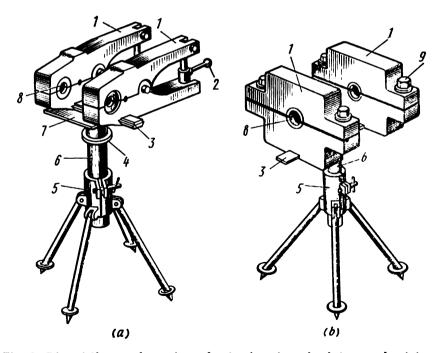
Dispositifs pour le soudage aluminothermique des brins en aluminium:
